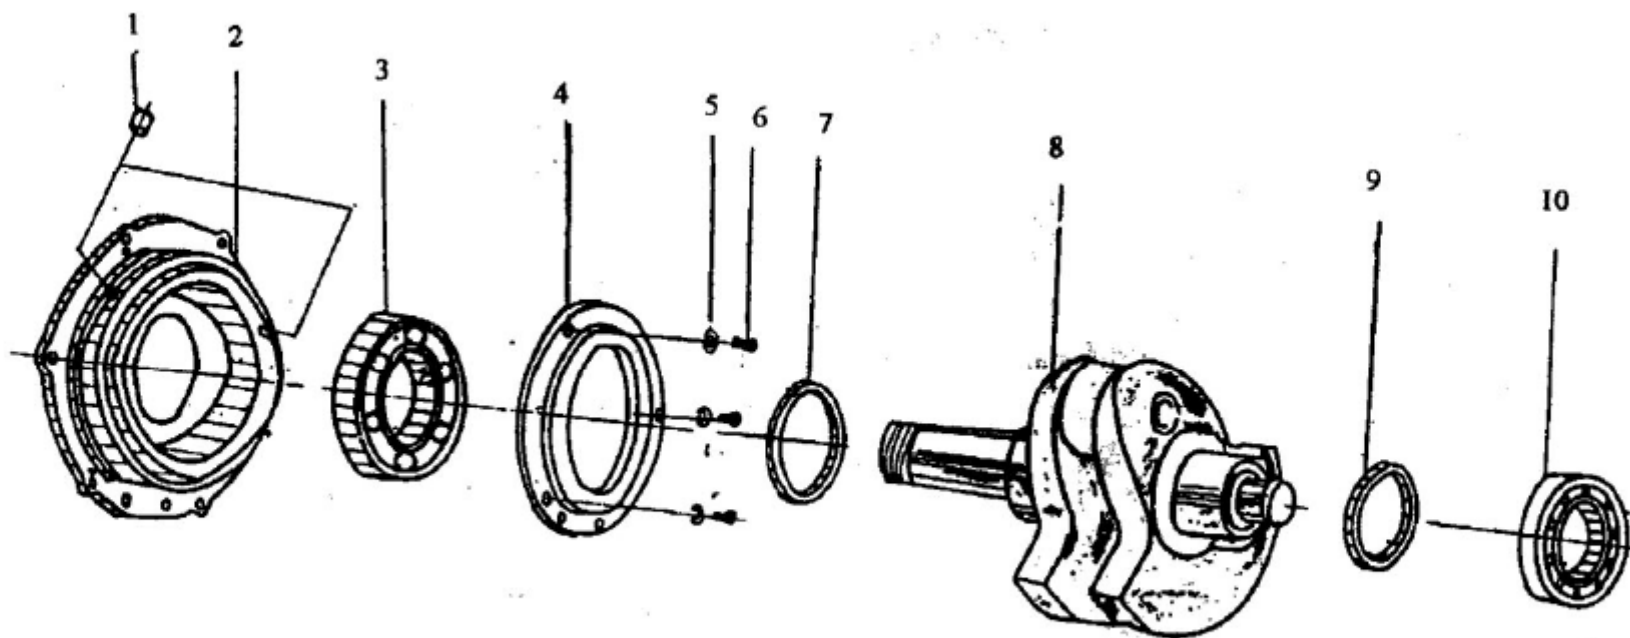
Сбор коленчатого вала поршневого соединительного штока и сбор маховика (b) –
